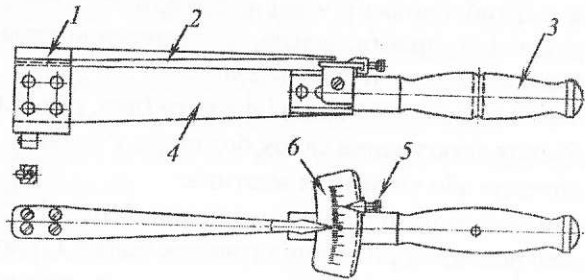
Динамометричний ключ зі шкалою-показчиком необхідного крутного моменту: 1 – головка; 2 – стрілка; 3 – рукоятка; 4 – лінійка; 5 – показчик; 6 – шкала
